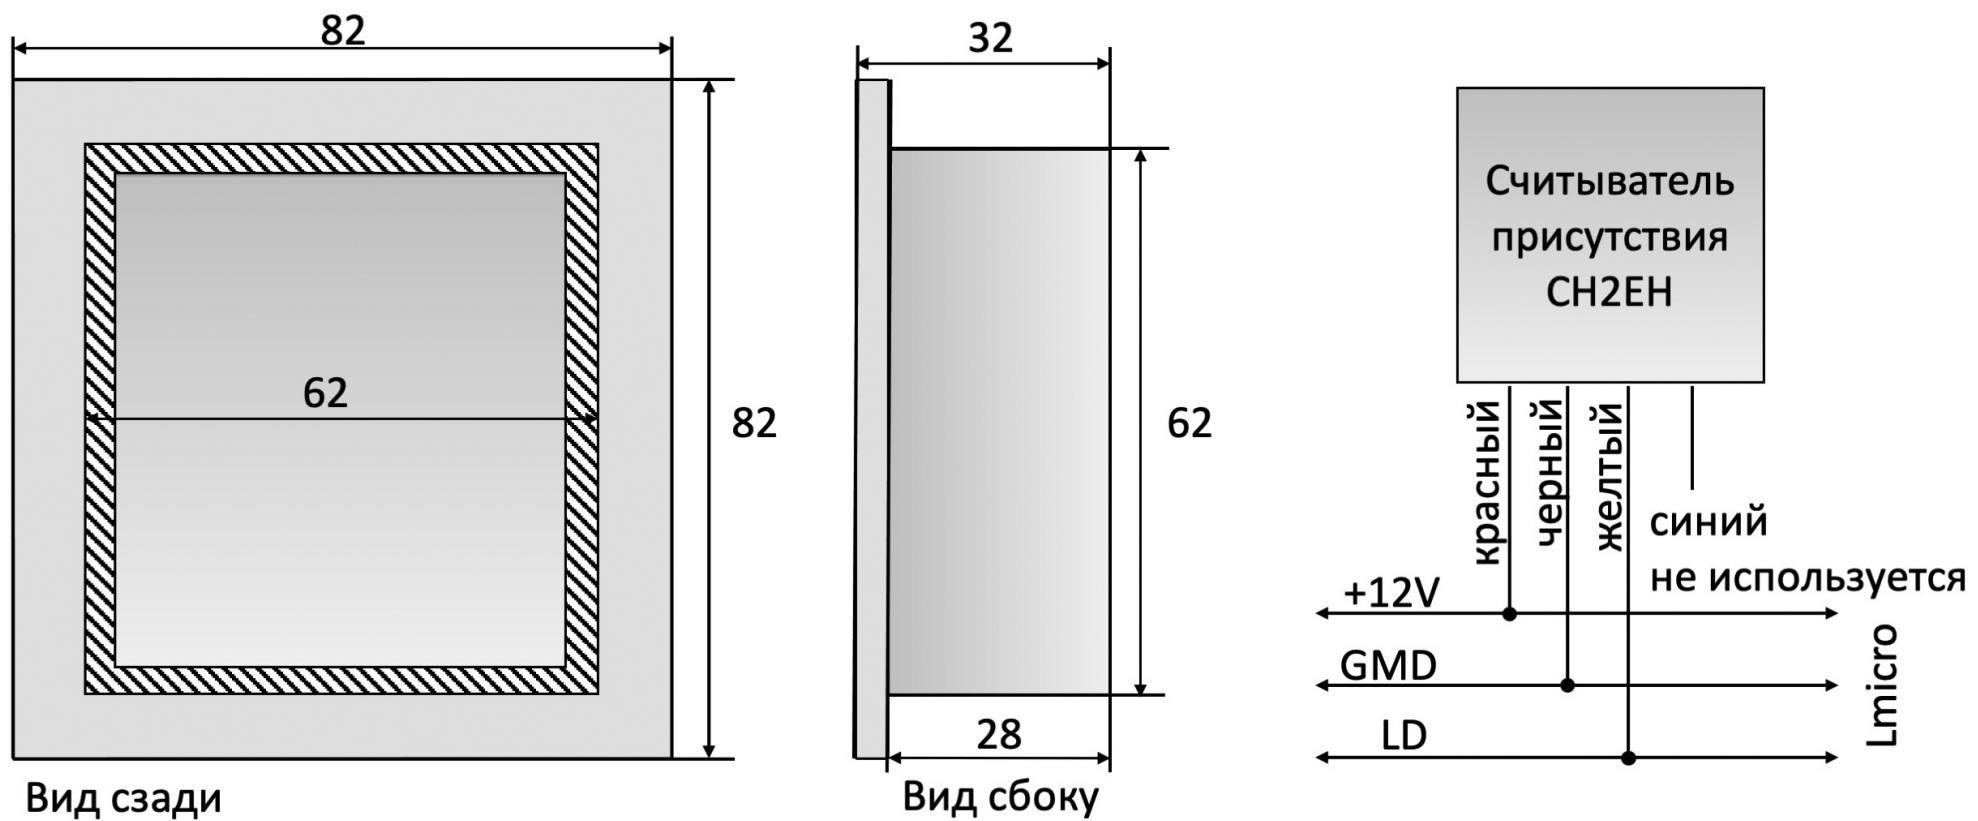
Размеры отверстия под считыватель и схема подключения адресного считывателя присутствия CH2EN
